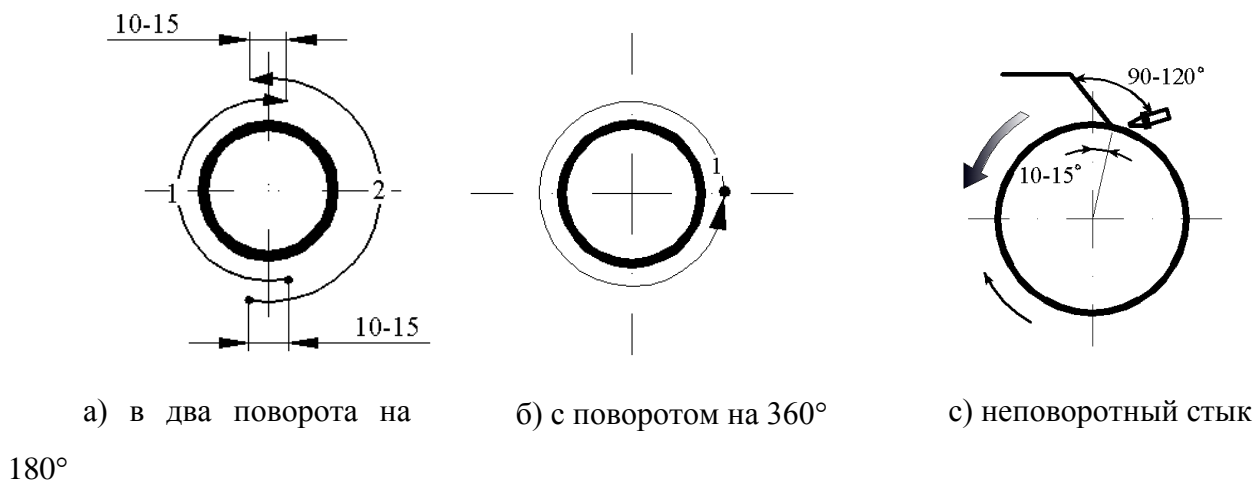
Схема выполнения сварного неповоротного и поворотного шва при газовой сварке
